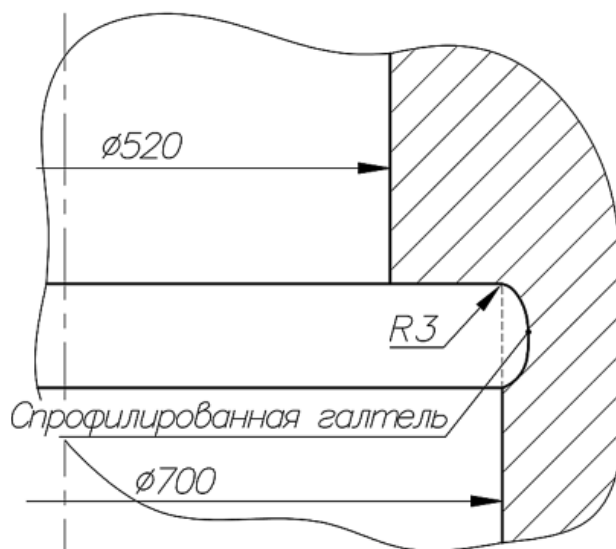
Конструкция галтельного перехода с заглублением в вертикальную стенку отверстия для установки гайки нажимного винта
